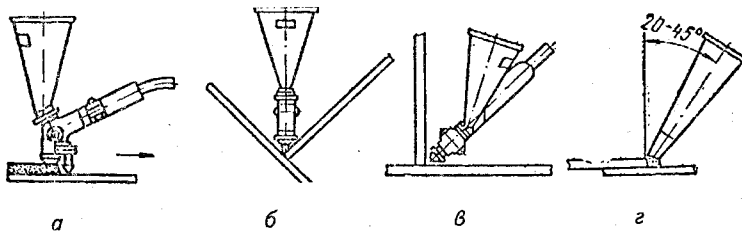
Схема полуавтоматической сварки под флюсом: а — стыковых швов; б — в положении «в лодочку»; в — тавровых швов; г — нахлесточных швов
